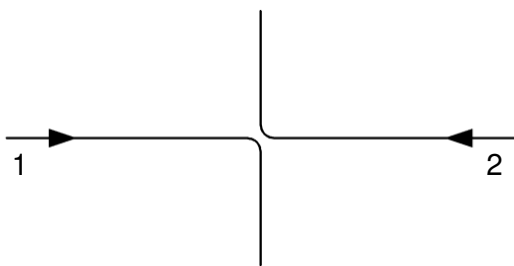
Schweißpfad Versuch 1 - Lage 1
